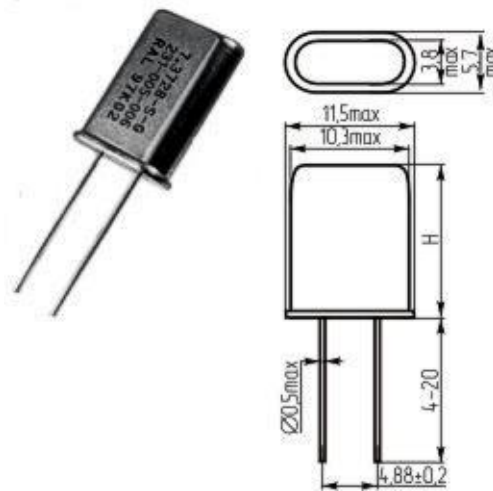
Габаритні розміри резонатора РК-02МД-Г
